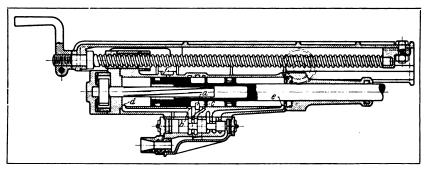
Bohrmaschine zur Befestigung an einer Spannsäule.
